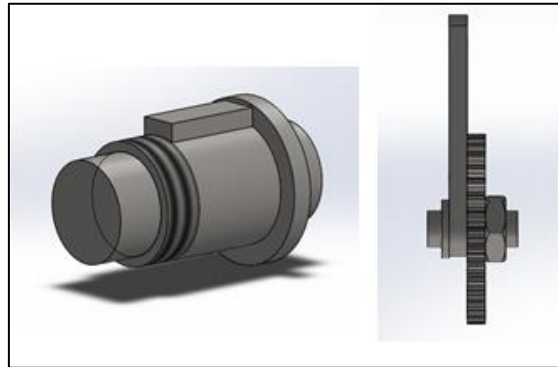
Eje libre (izquierda). Eje junto con el gancho, engranaje y tuerca (derecha).
